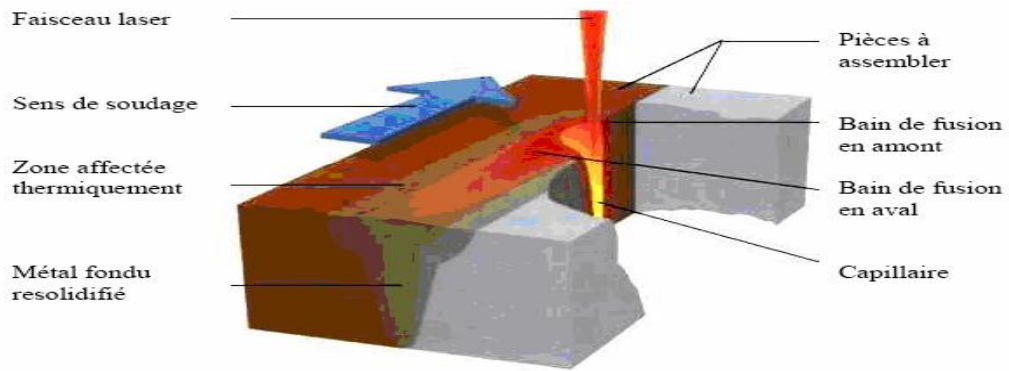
Principe du soudage par faisceau laser [4].
